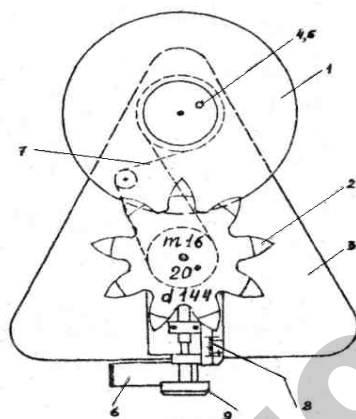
Принципиальная схема прибора ТММ-47А для нарезания зубчатых колес долбяком: 1 – диск для закрепления заготовки; 2 – долбяк; 3 – станина; 4, 5 – закрепляющие шайбы; 6 – рычаг храпового механизма; 7 – стальная нить; 8 – шкала; 9 – фиксатор сдвига долбяка
